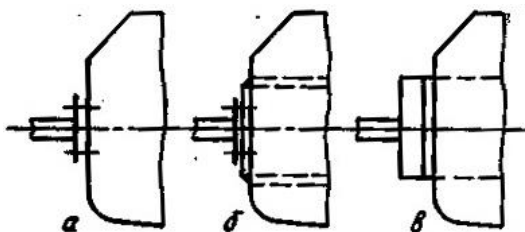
Схема кріплення опорно-поворотних цапф до корпусу (а), до підсиленого корпусу (б) і до опорного кільця (в).
